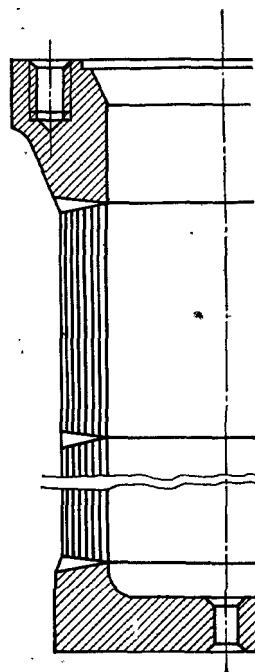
Многослойный корпус с приварными фланцем и дном.
